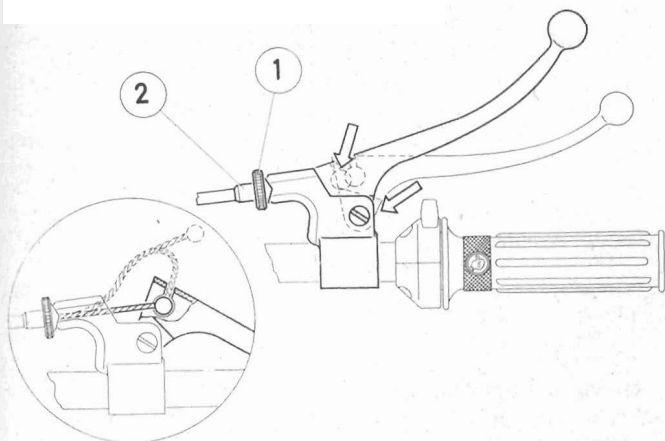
Mando freno delantero: Reglaje y engrase.
